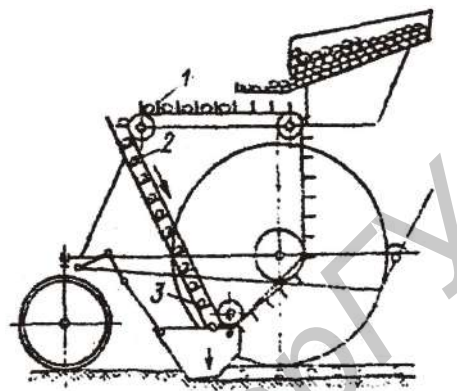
Схема рабочего процесса картофелесажалки КП-2: 1 — металлические пластинки; 2 — цепи; 3 — выводные рукава
